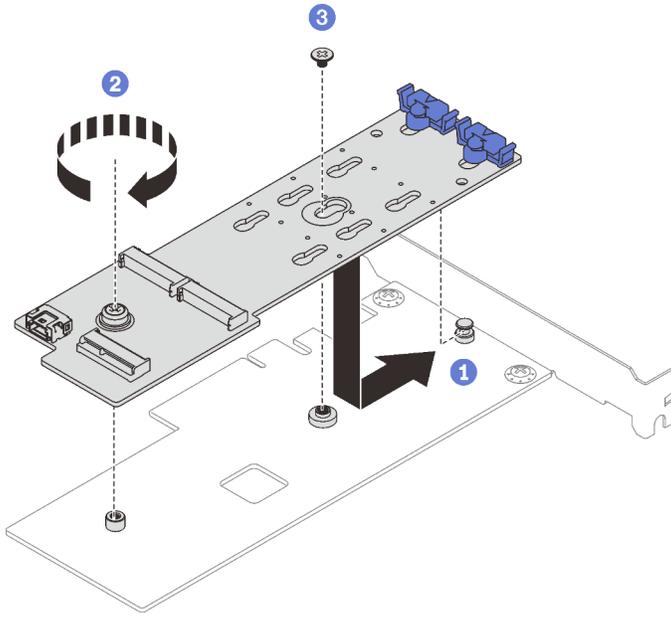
Befestigen des M.2-Bootadapters am PCIe-Adapter
